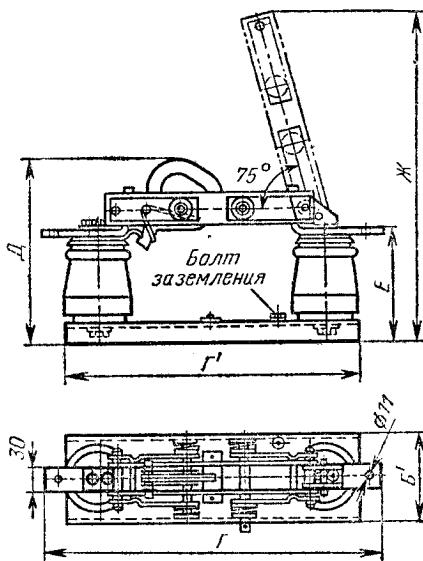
Разъединитель однополюсный РВО-6-10.
